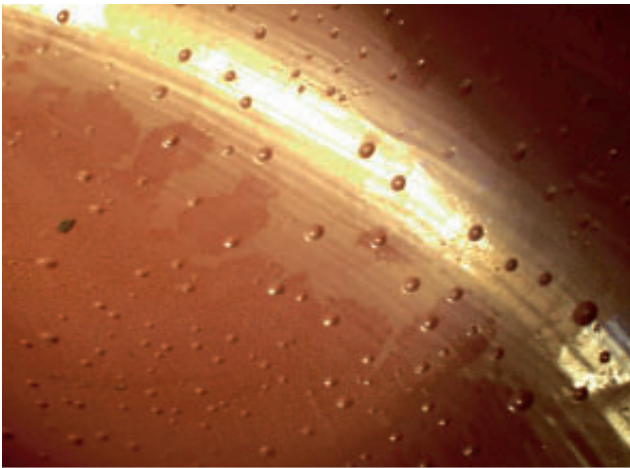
Blasenbildung einer Epoxydharzbeschichtung auf kontaminiertem Stahluntergrund
